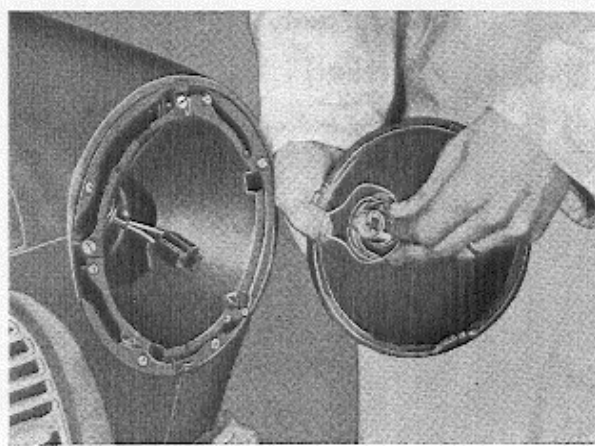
Ausbau der Haltefeder für die Glühbirne
